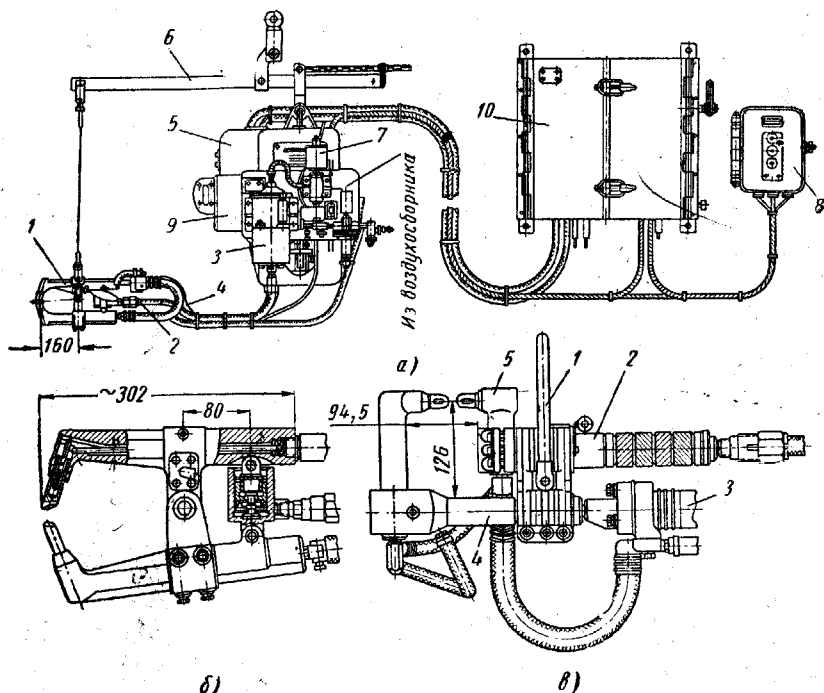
Сварочный пистолет (а) и схема устройства шин для получения контура постоянных размеров при сварке распорным пистолетом (б).
